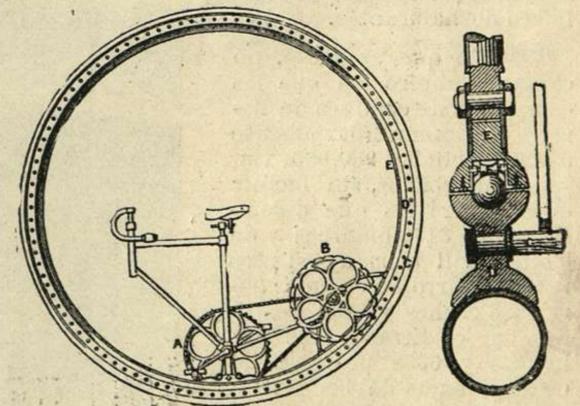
CORTE Y DETALLES DEL MECANISMO.
